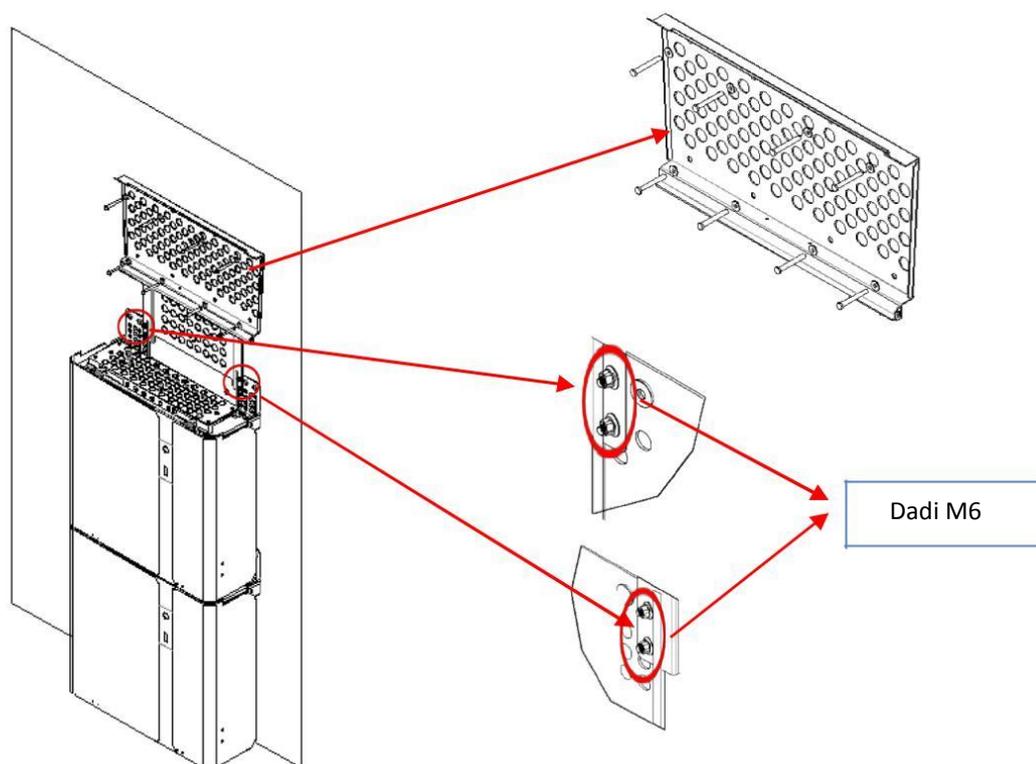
Installazione del sistema di fissaggio a servizio dell'inverter
